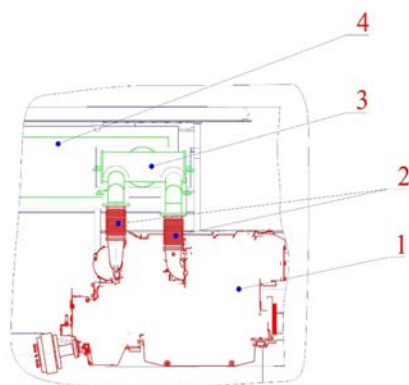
Схема компоновки СЕУ з ТАС (вид збоку): 1 – дизельний двигун, 2 сифонні компенсатори, 3 – патрубок газоходу, 4 – глушник-теплоакуюлятор
